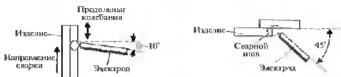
Положение электрода при сварке нахлесточного соединения в вертикальном положении снизу вверх
